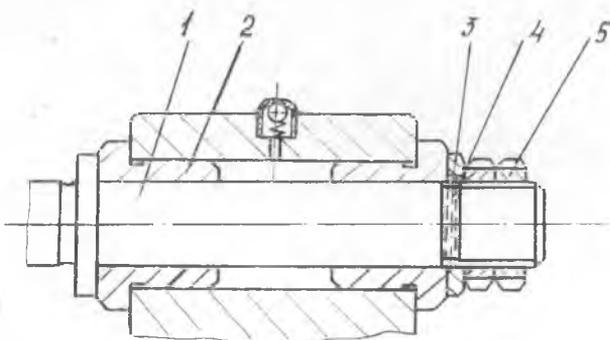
Шпindelь цилиндрический: 1—палец; 2—втулка; 3 — шайба; 4 — шуп; 5 — гайка
